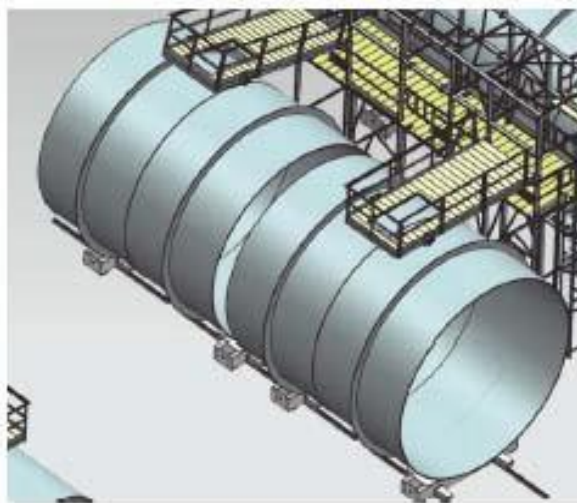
Exemplo de plataforma soldadura circunferencial
